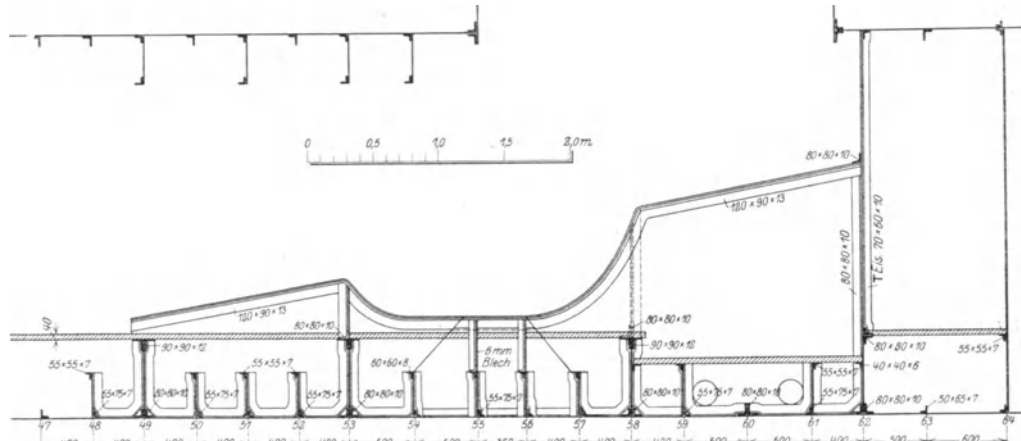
Maschinenfundament in Seitenansicht. Radschlepper.
